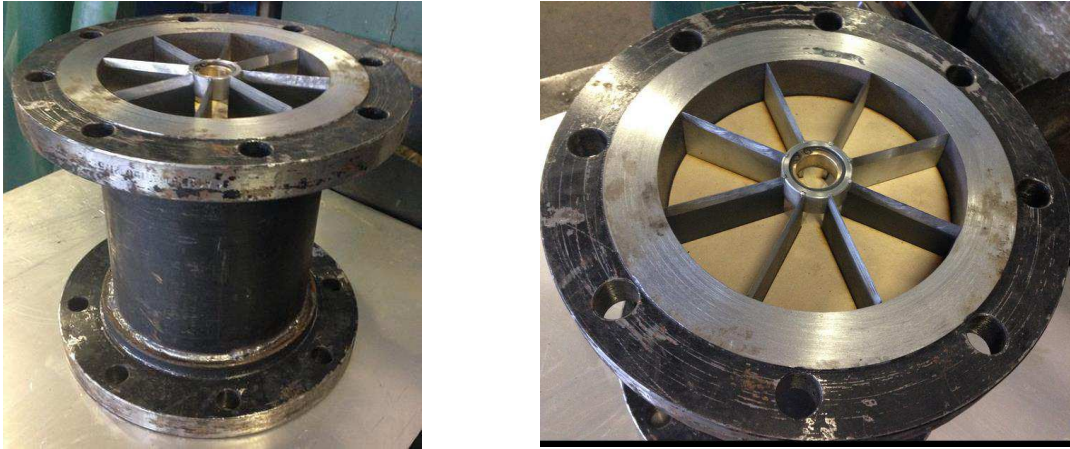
Flanjes soldados y aletas en proceso de soldadura
